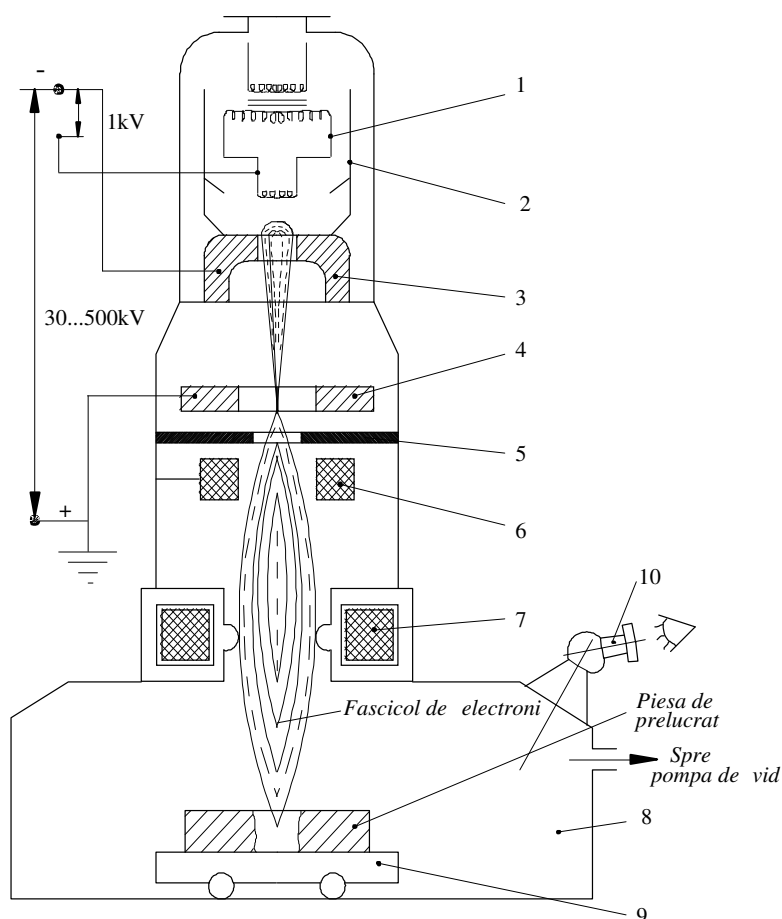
Schema de principiu a unei instalații de prelucrare dimensională cu fascicul de electroni:
